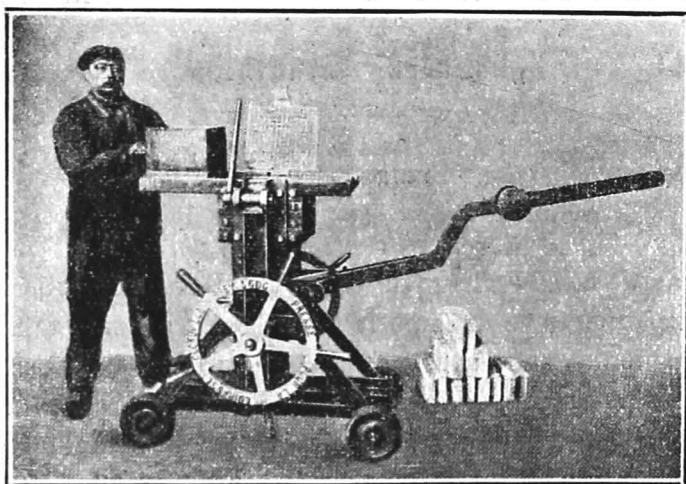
Introducerea în presă a mortarului pentru fabricarea cărămizei.
